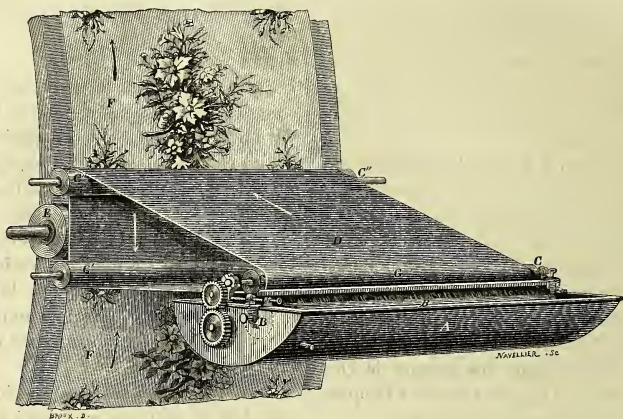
Divers éléments de la machine à imprimer les papiers peints.
